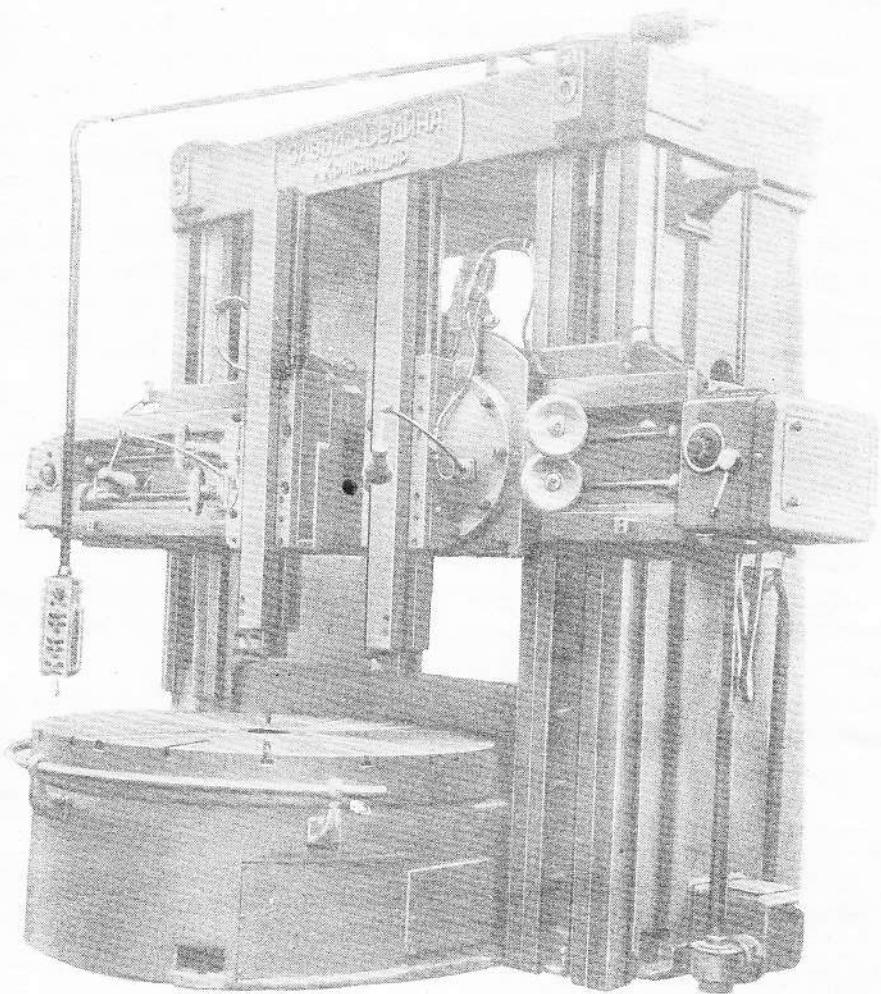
Рис. I. Двухстоечный токарно-карусельный станок модели 1М553
